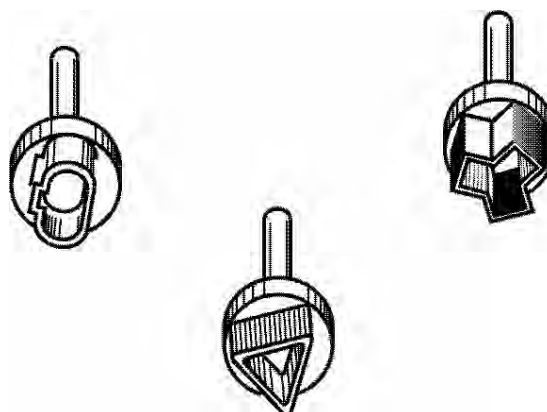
Примеры ультразвуковых инструментов для вырезания деталей сложной формы
